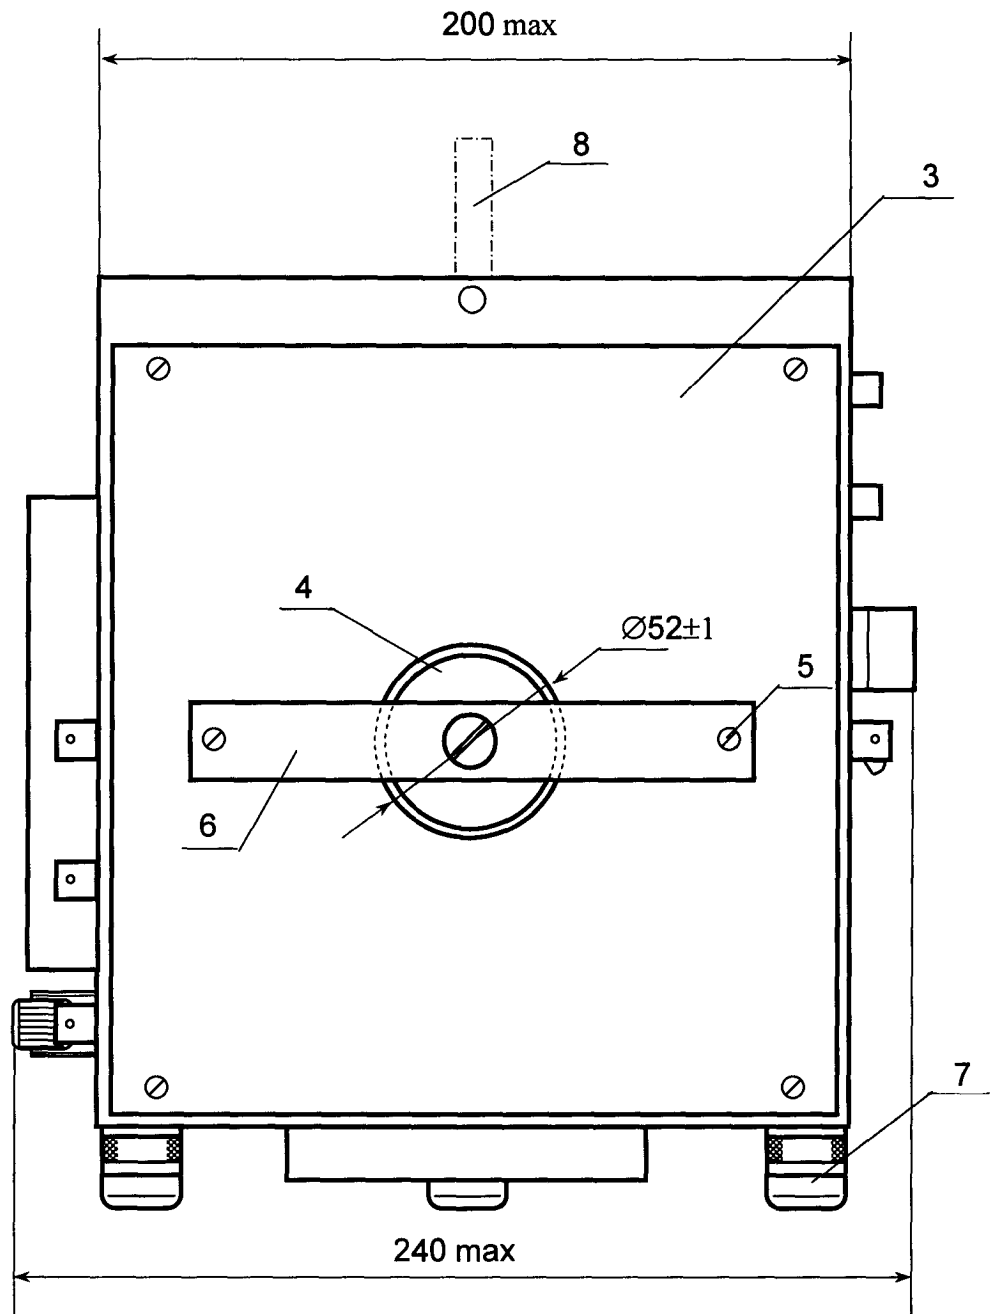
Внешний вид ( со стороны левой боковой панели) и габаритные размеры вибростенда ВСП-131
